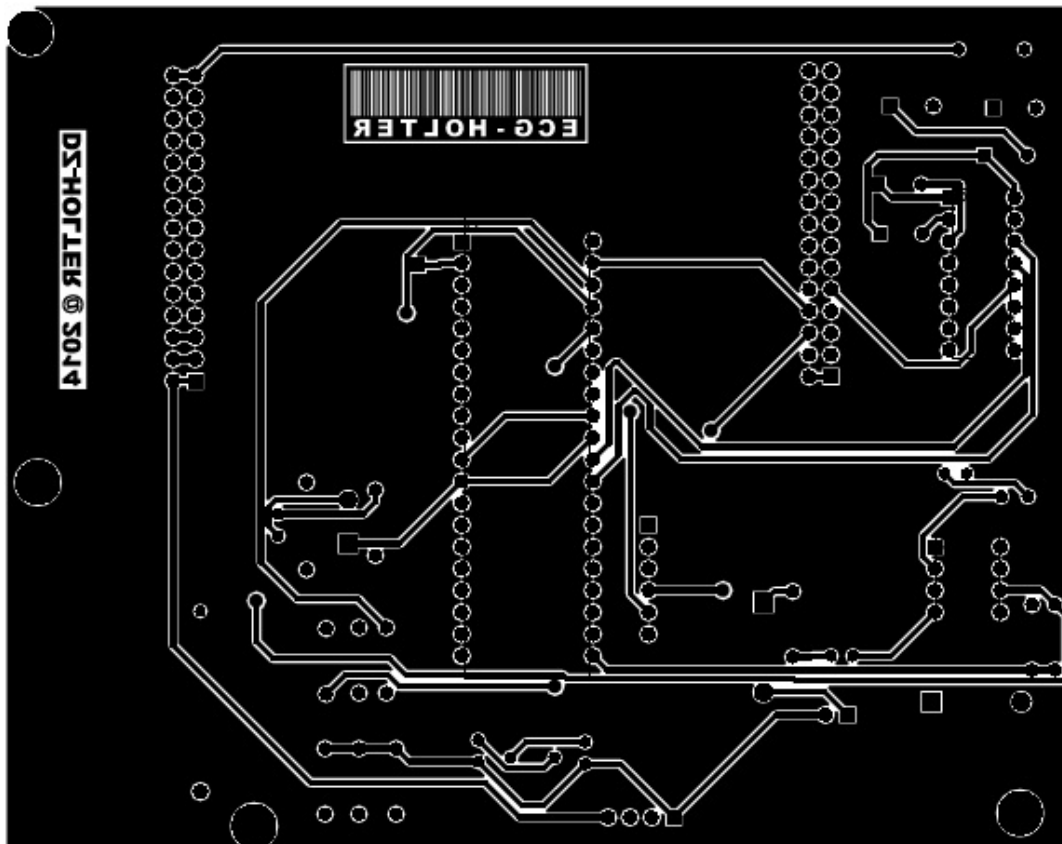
Typon de la face soudure de la carte numérique.
